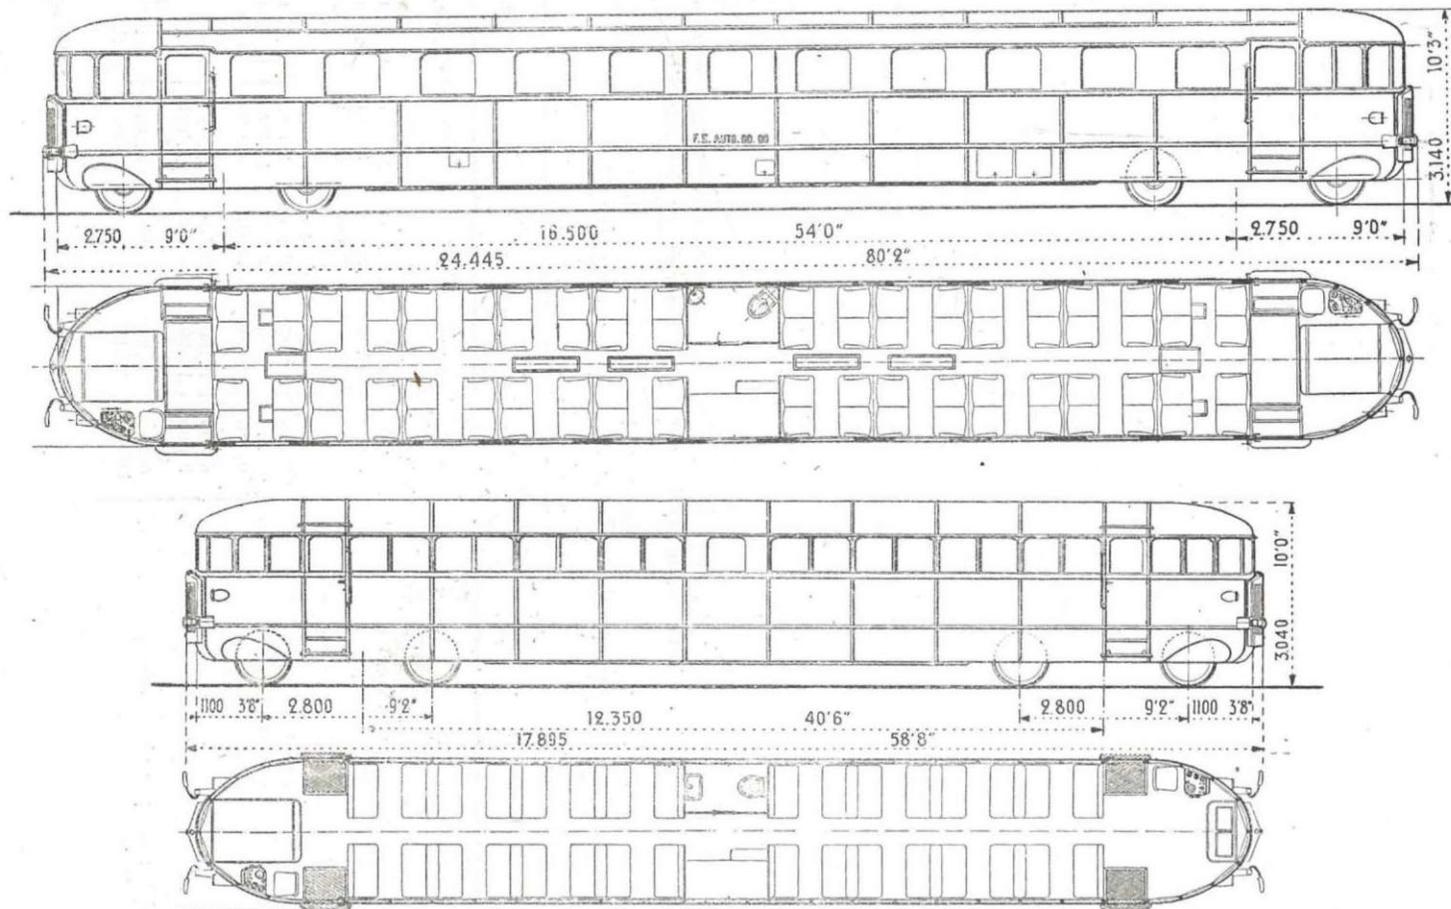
Autorails Fiat à 80 et à 64 places.
